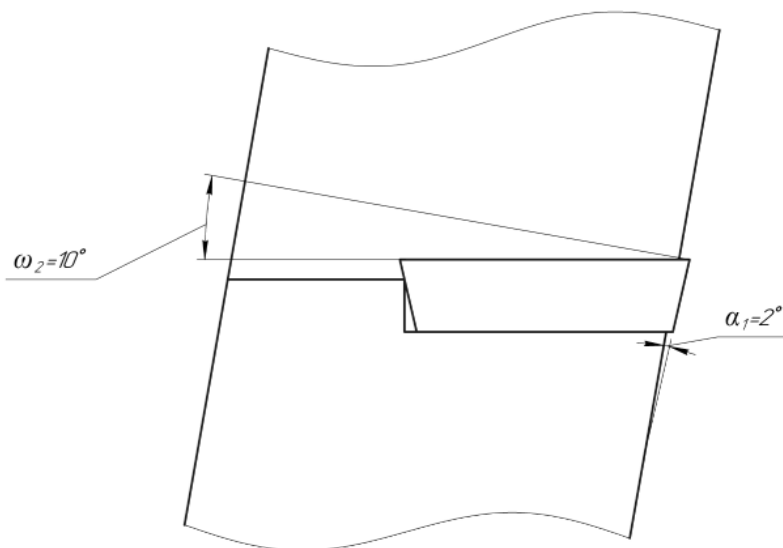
Установка корпусу на фрезерному верстаті
